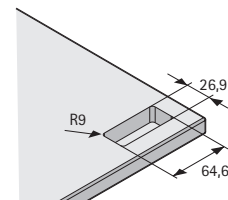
Fräsbild zum Einbau des Handschalters LegaDrive Touch Inlay Basic mit Gummilamellen
